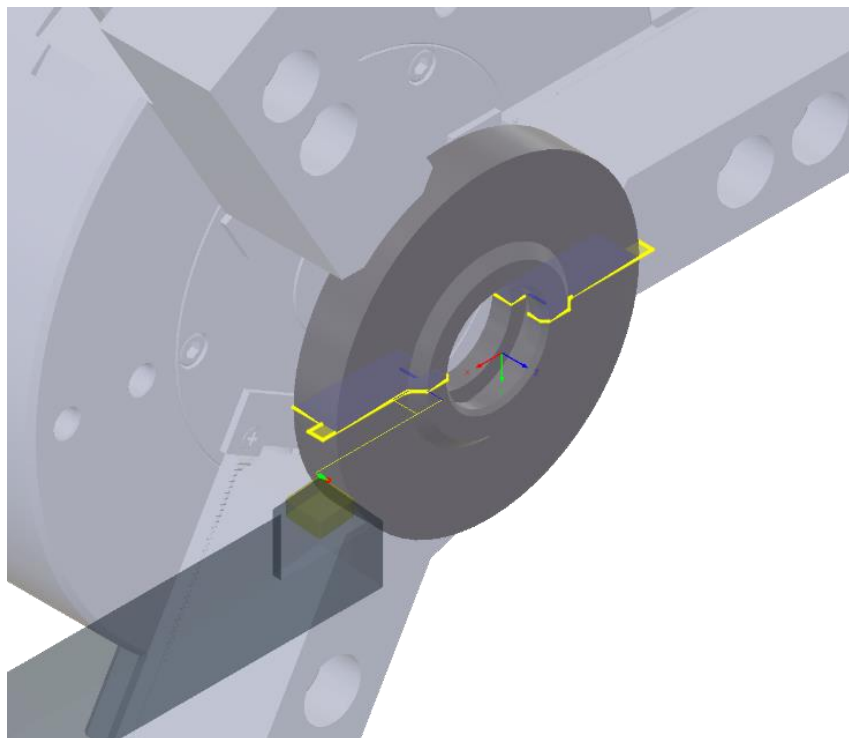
Зображення переходу точіння фаски буртика заготовки
